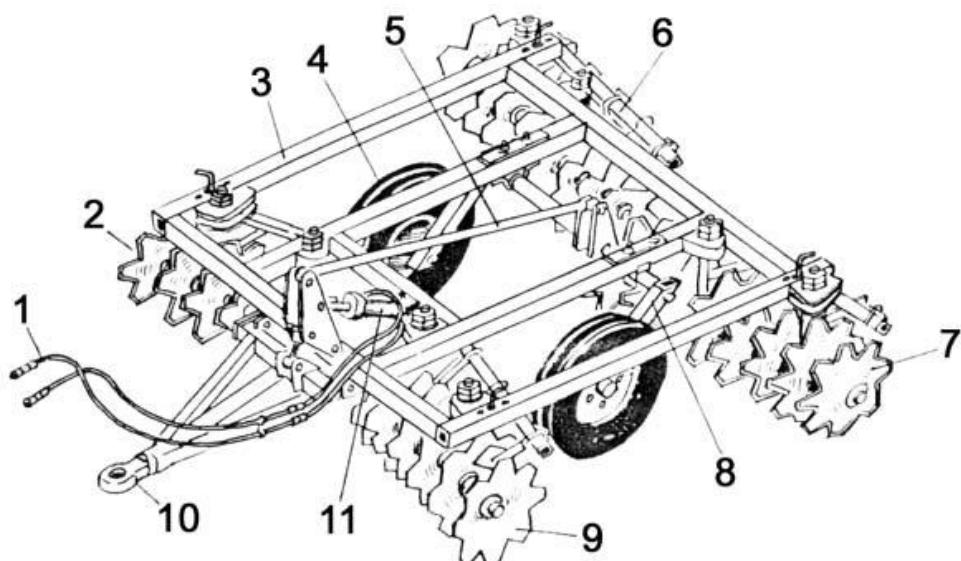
ОБЩИЙ ВИД БОРОНЫ ДИСКОВОЙ ТЯЖЕЛОЙ Л-113-02
